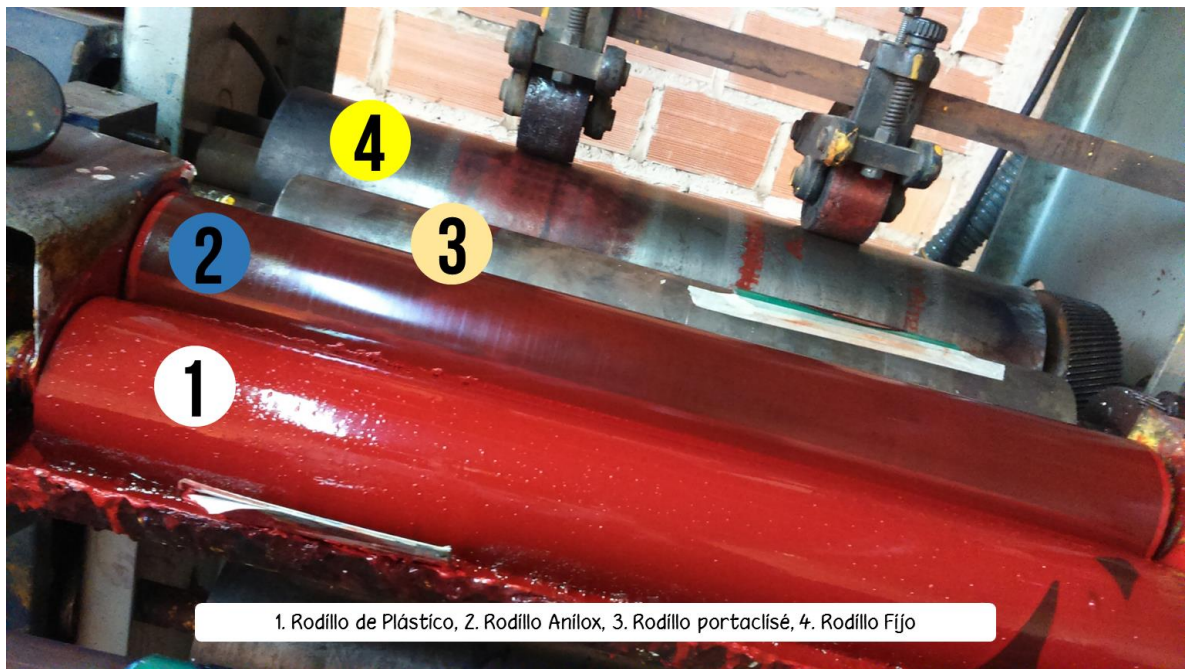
Elementos rodantes principales de la impresora (Rodillos)
